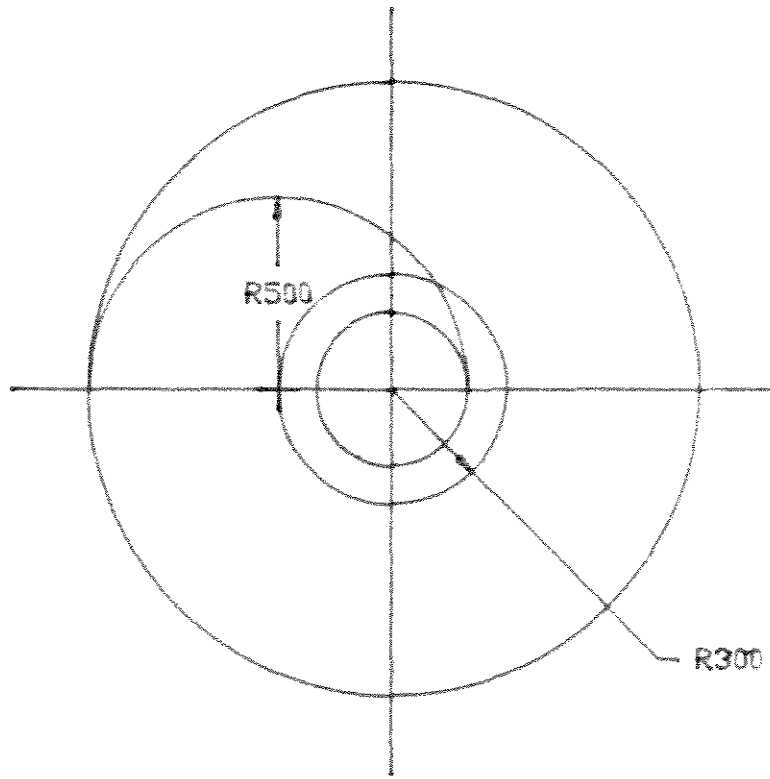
RR=500mm e RC=300mm.
